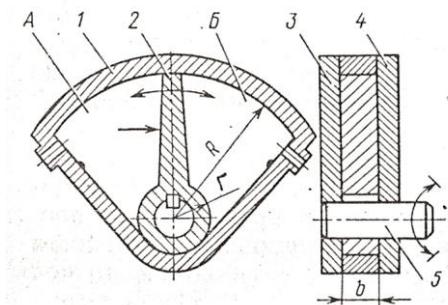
Пластинчатый поворотный гидродвигатель: 1 - корпус; 2 - пластина; 3, 4 - крышки; 5 - силовой вал.
